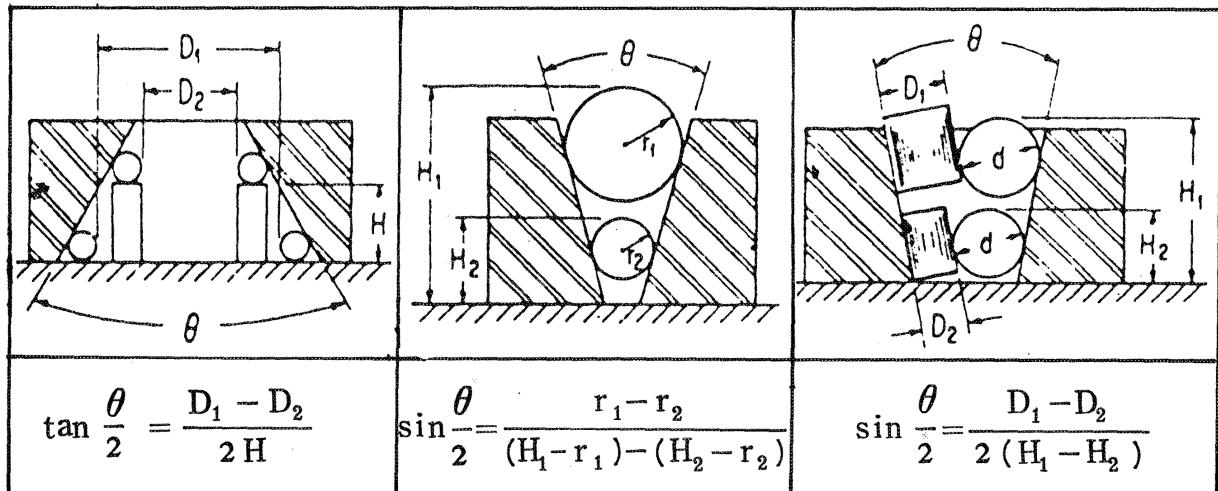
內錐測量法（選自 HANDBOOK OF DIMENSIONAL MEASUREMENT）
